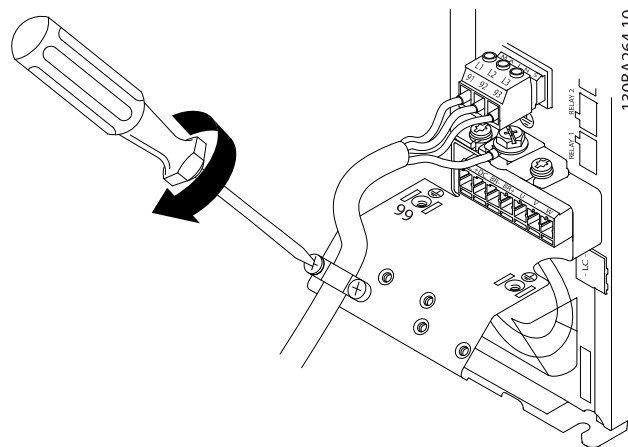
Por último, apriete la abrazadera de montaje de los cables de alimentación.
